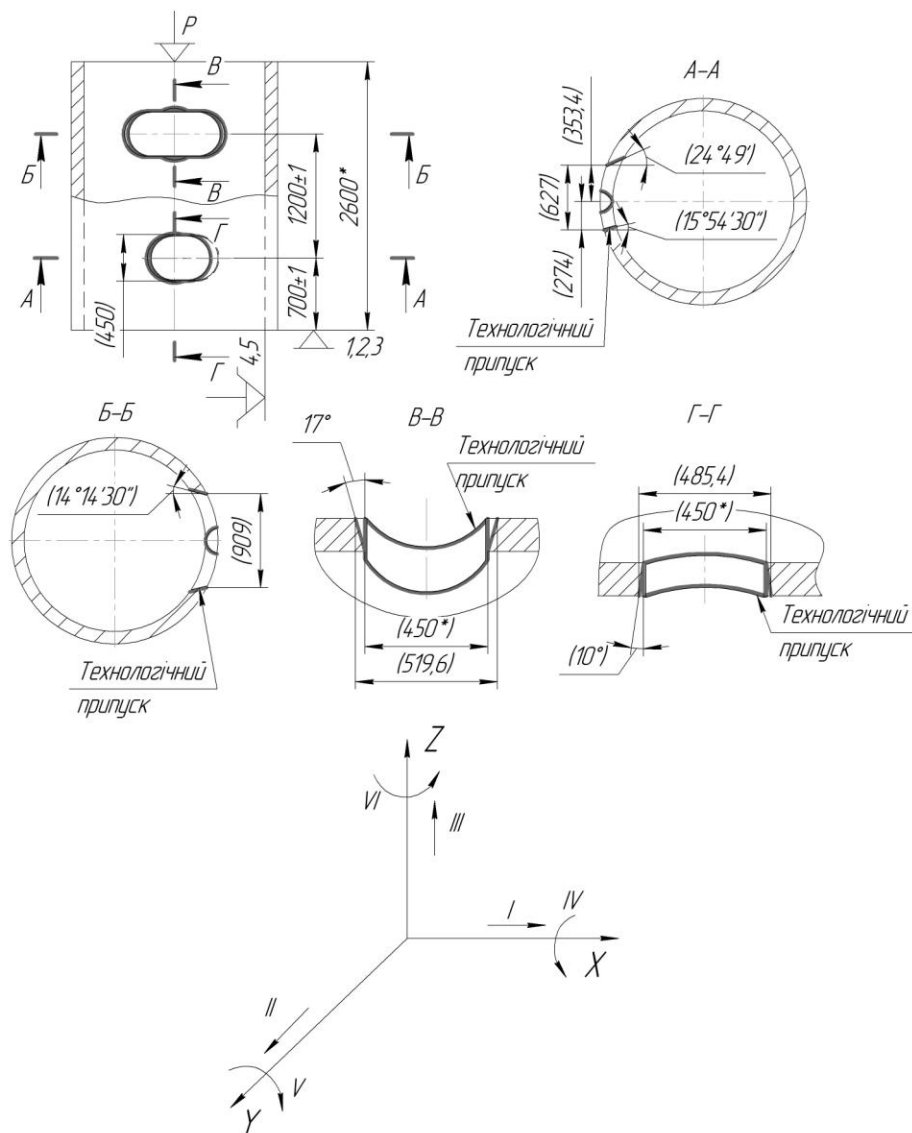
Схема базування заготовки в пристосуванні
